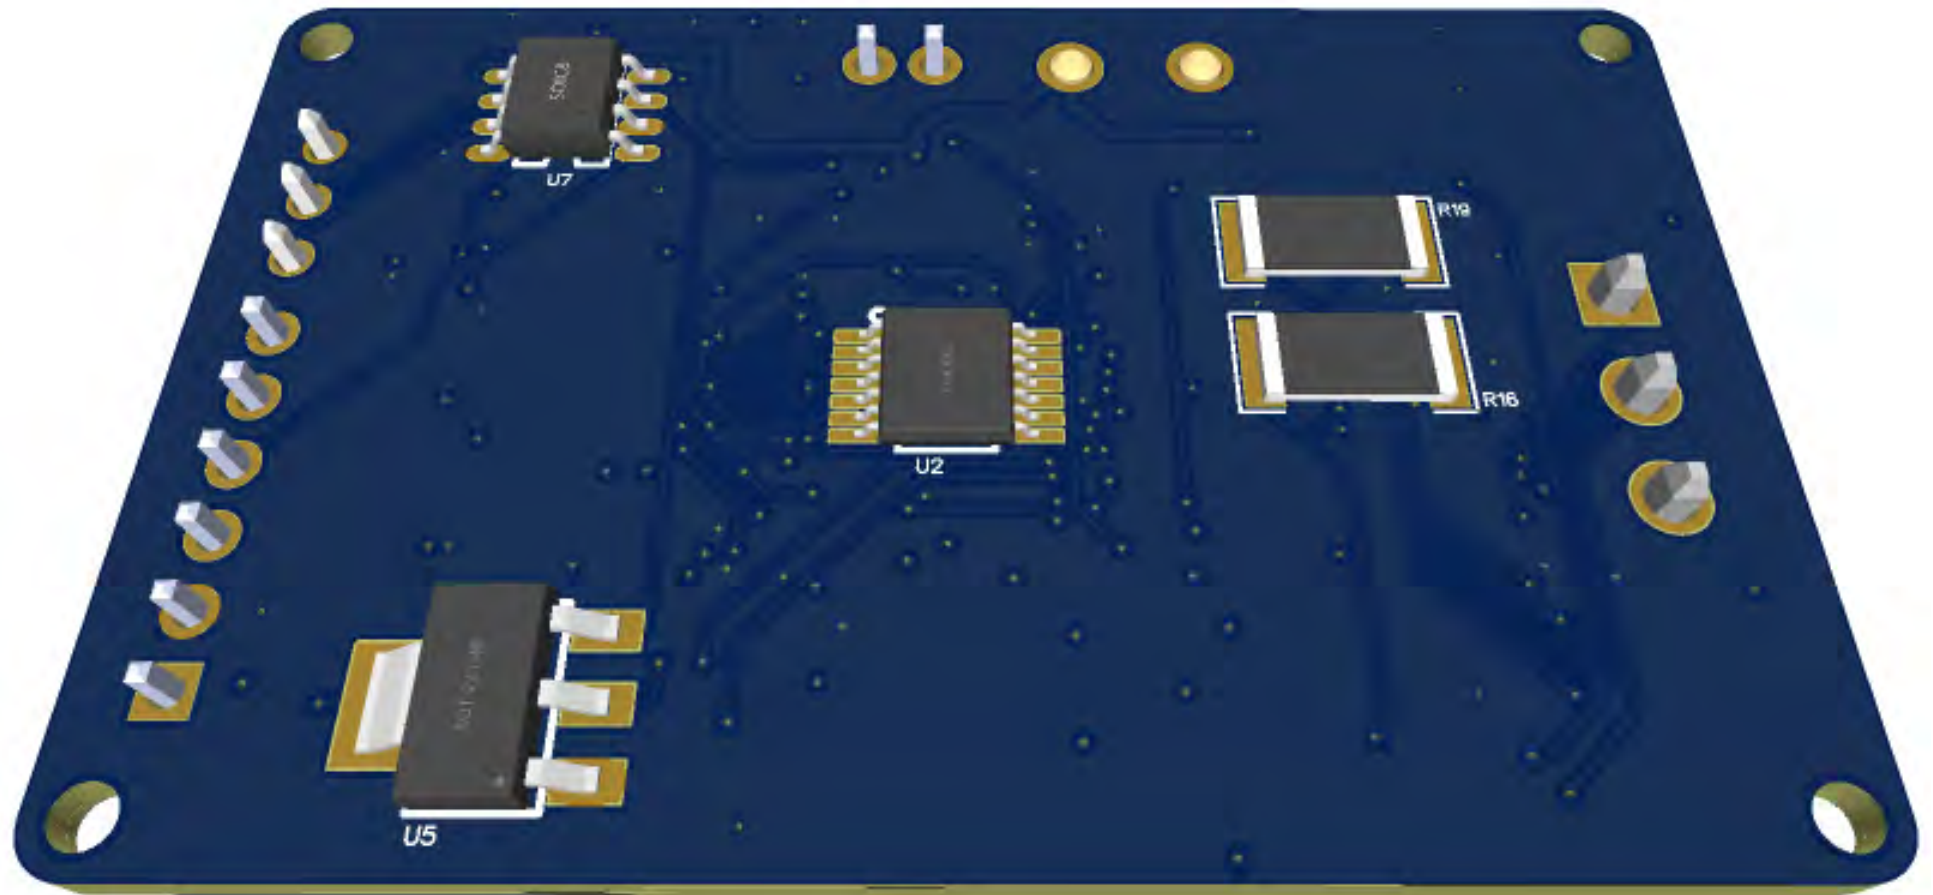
Modelado 3D de la tarjeta PCB – capa inferior
